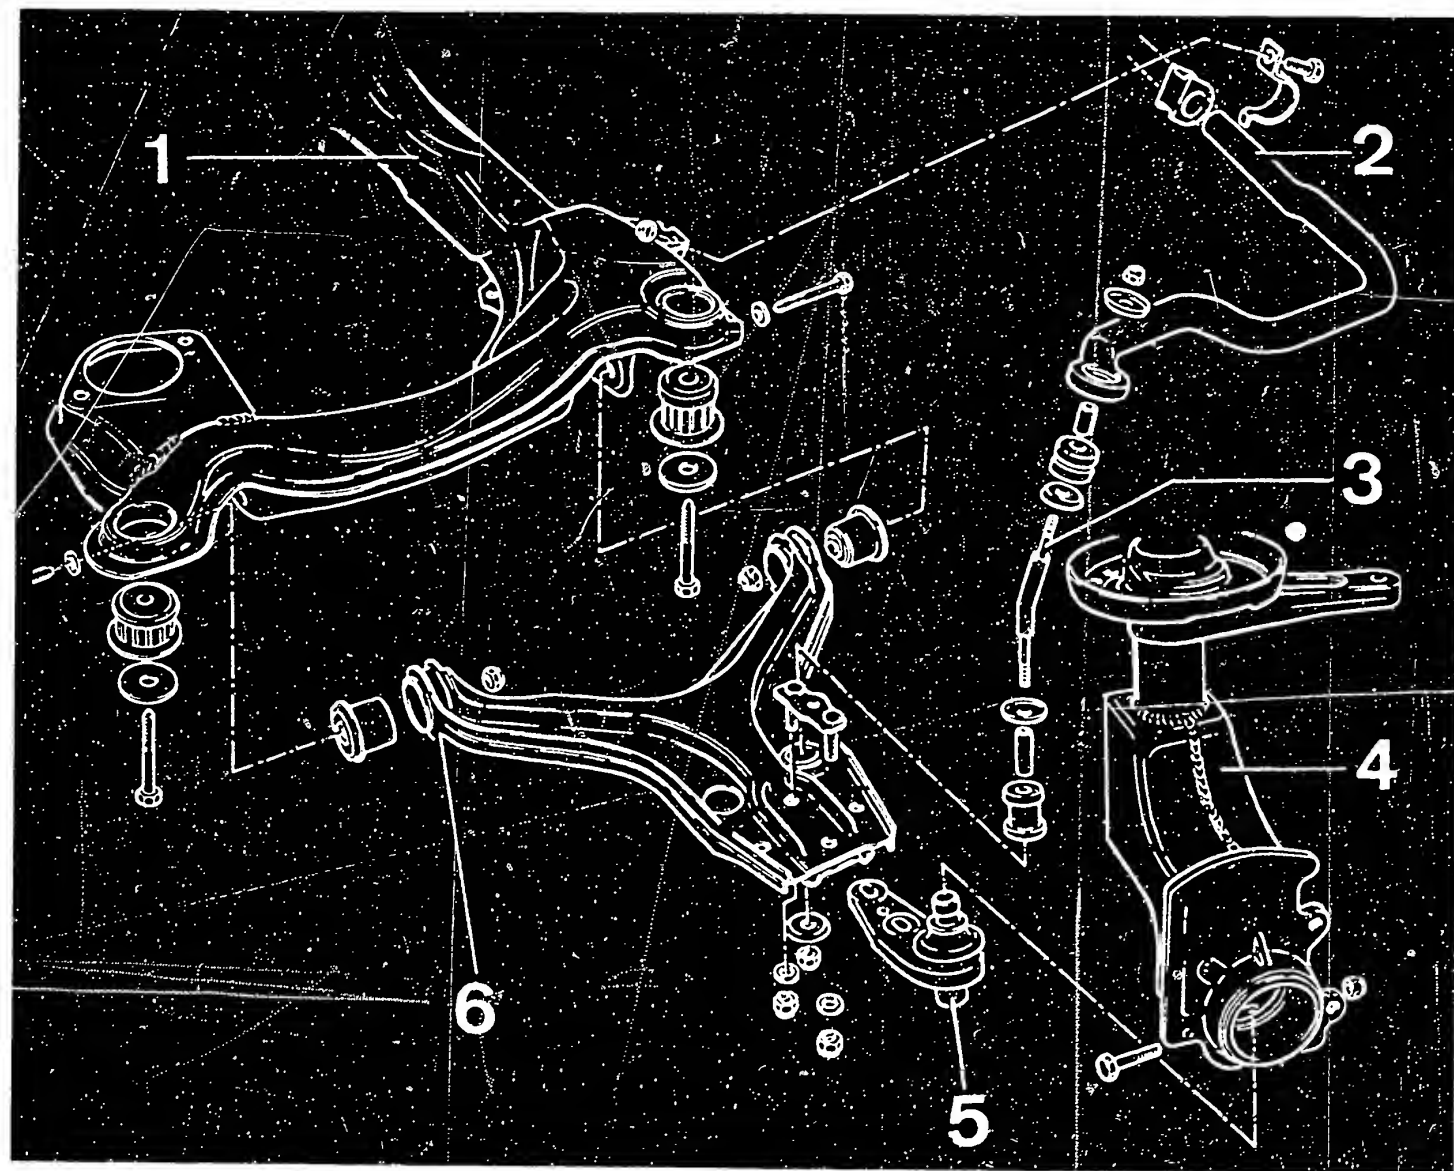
Einzelteile der vorderen Radaufhängung: 1 Aggregatträger – 2 Querstabilisator – 3 Verbindungsstange – 4 Radlagergehäuse – 5 Kugelgelenk – 6 Querlenker.
